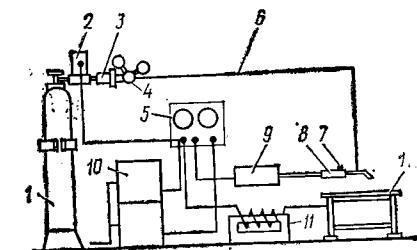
Схема установки для полуавтоматической сварки в углекислом газе:
